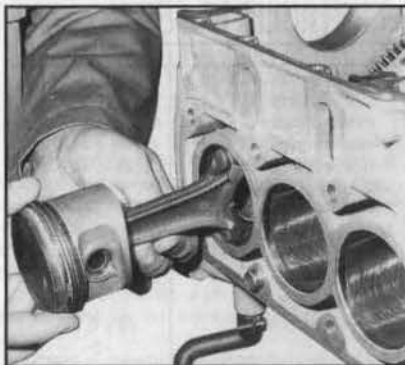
Desmontaje del conjunto pistón-biela por el lado del plano de junta de la culata (foto RMT)
